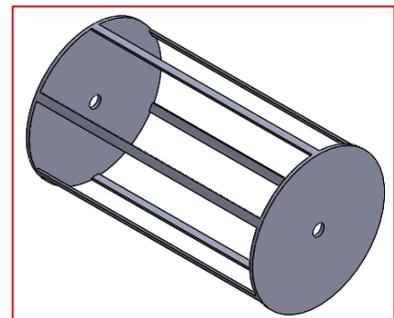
Croquis del "esqueleto" del tambor cilíndrico
